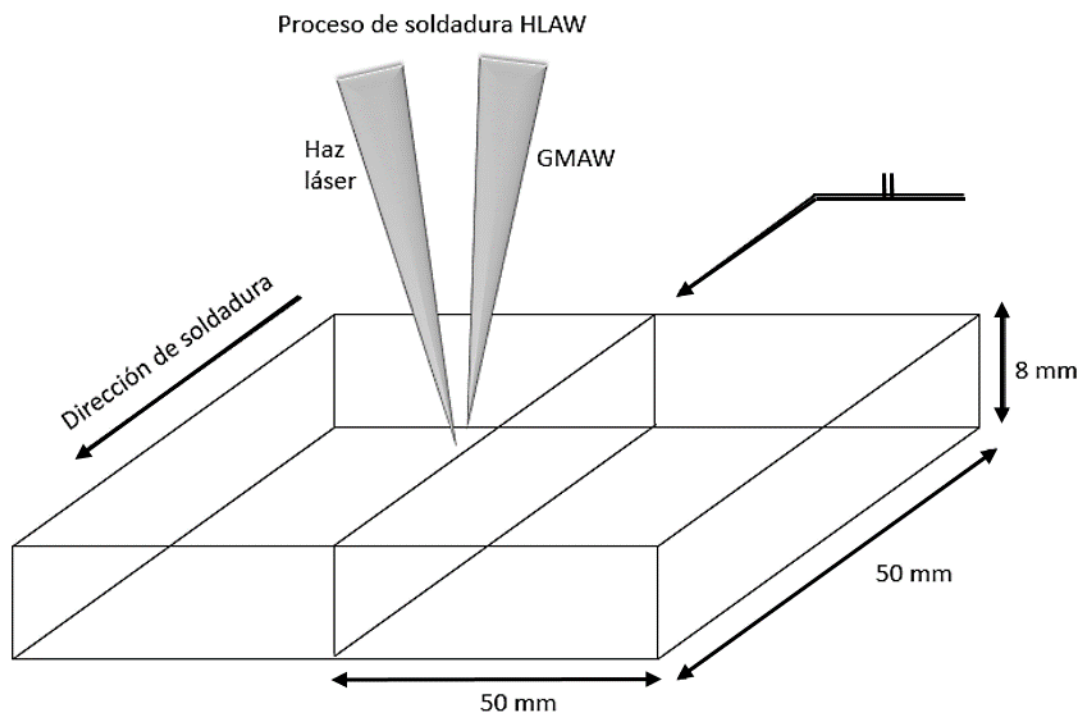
Representación esquemática de dimensiones y diseño de unión.
